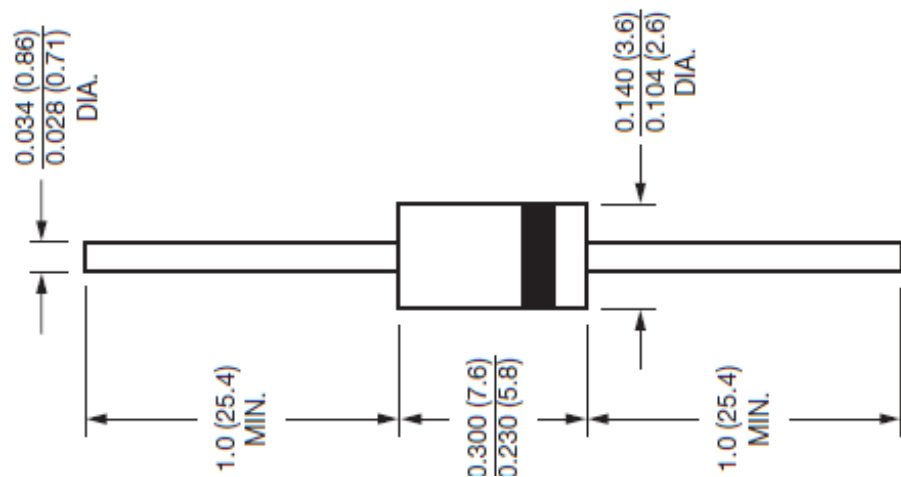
Габаритні розміри діоду Шоттки SB220
